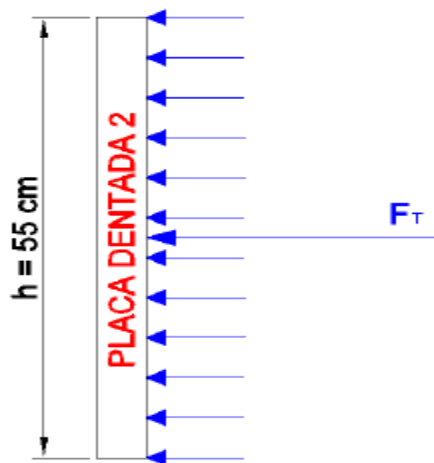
Fuerzas uniformemente repartidas en placa dentada 2 o placa dentada fija.
